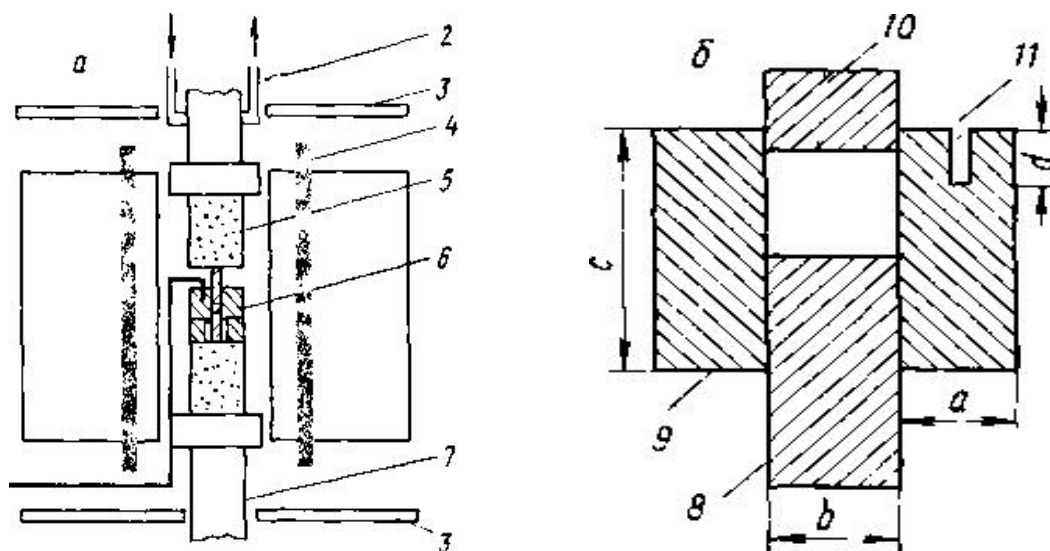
Схема установки (а) и пресс формы(б) для горячего прессования: 1 — термопара; 2 — система водного охлаждения; 3 — металлическая теплоотражающая плита; 4 — нагревательный силитовый стержень; 5 — корундовый стержень для передачи давления; б — пресс форма; 7 — подвижный пуансон; 8 — нижний пуансон; 9 — корпус формы; 10 — верхний пуансон; 11 — щель для термопары
